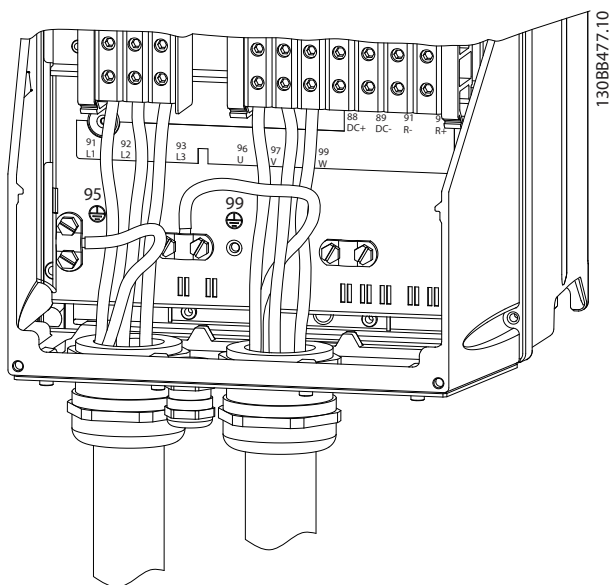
Проводка двигателя, питания и заземления для типоразмера А
